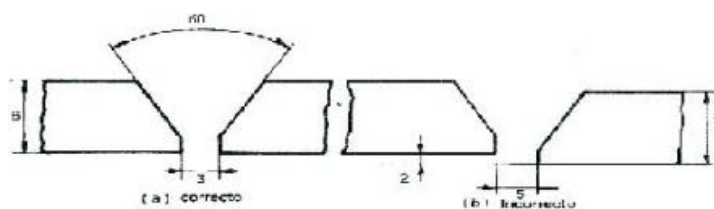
Posiciones relativas de los bordes de soldadura de formas correctas e incorrectas
